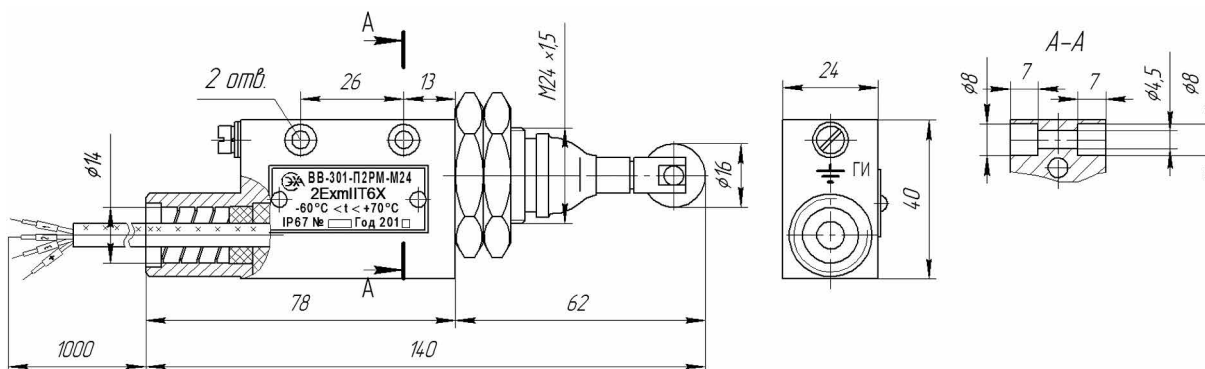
Габаритные и установочные размеры ВВ-301-П2РМ-М24
